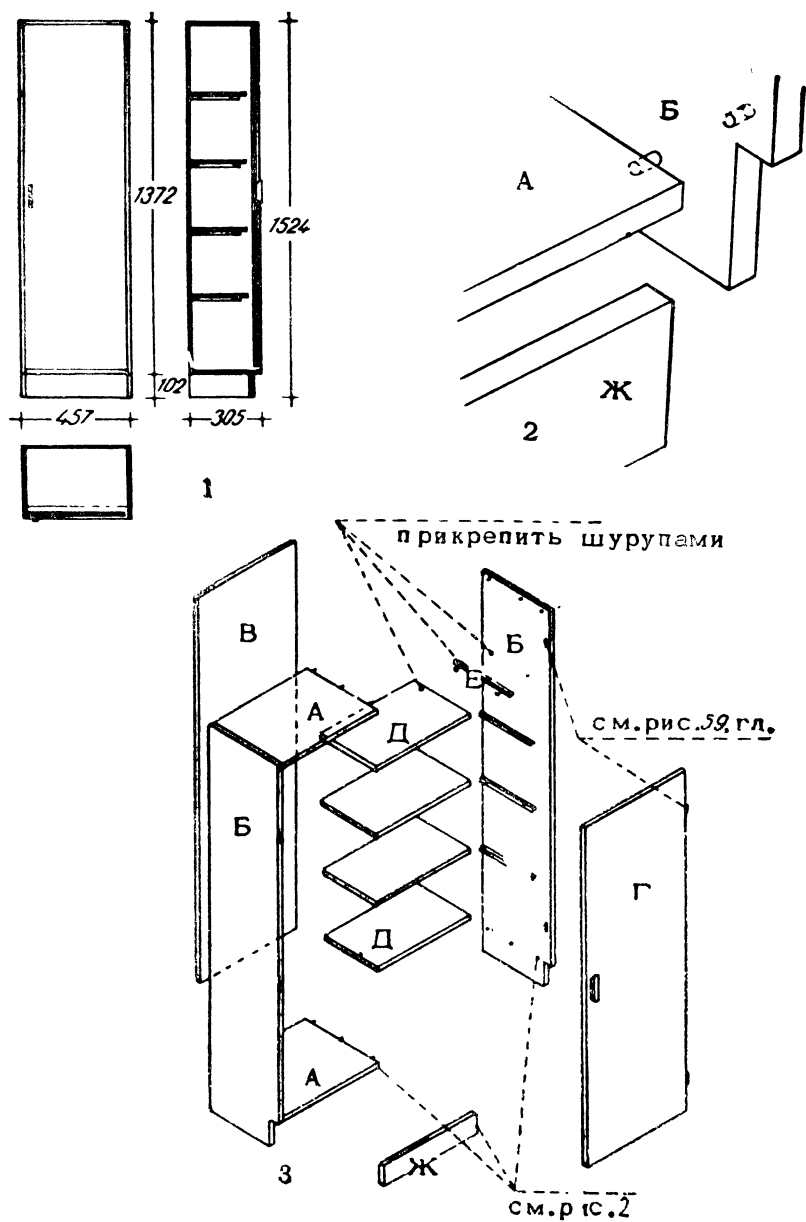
3. 1—вид спереди и разрезы; 2—эскиз соединения боковой стенки с нижним полком и продольным брусом плинтуса; 3—эскиз сборки деталей.
